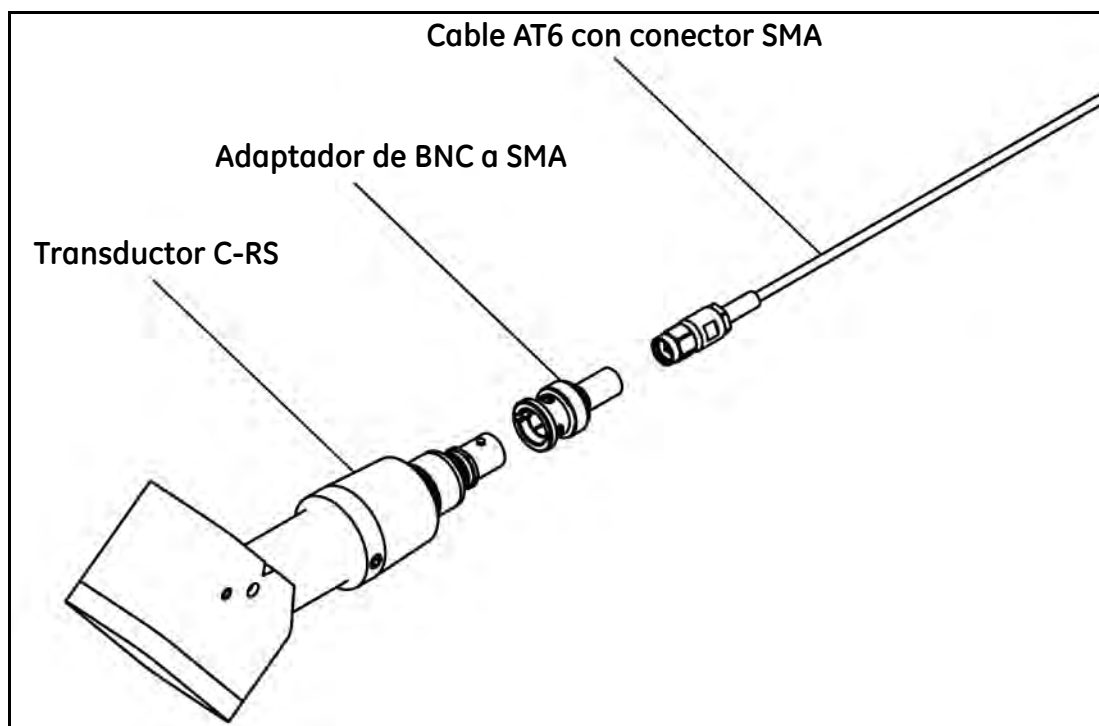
Instalación del adaptador de cable para el transductor C-RS
